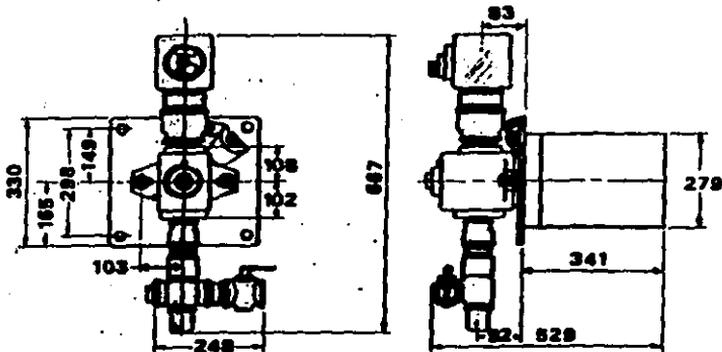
4 Dimensiones básicas del quemador 128 NH completo marca "Eclipse" (acotado mm).
